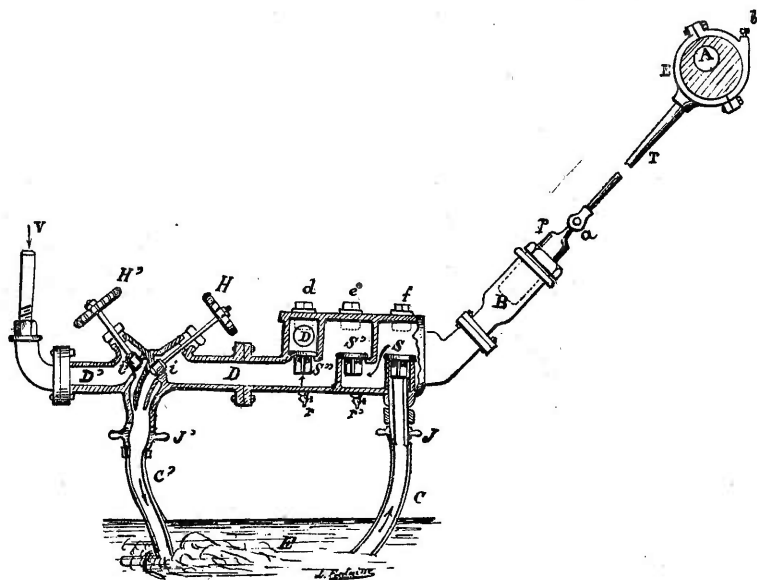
Coupe de la pompe alimentaire Garrett.
